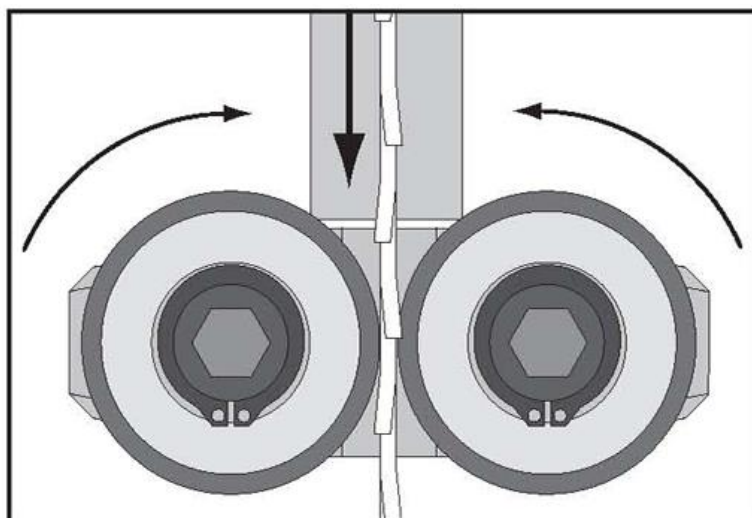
Направляющие подшипники пильного полотна равномерно и слегка соприкасаются с боковыми сторонами полотна.
